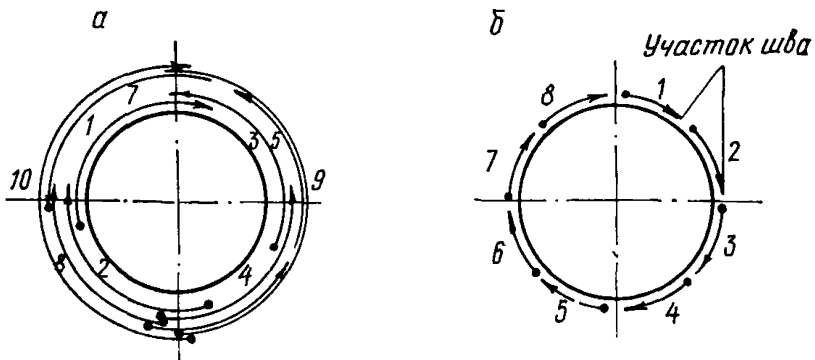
Сварка стыков труб различных диаметров:
